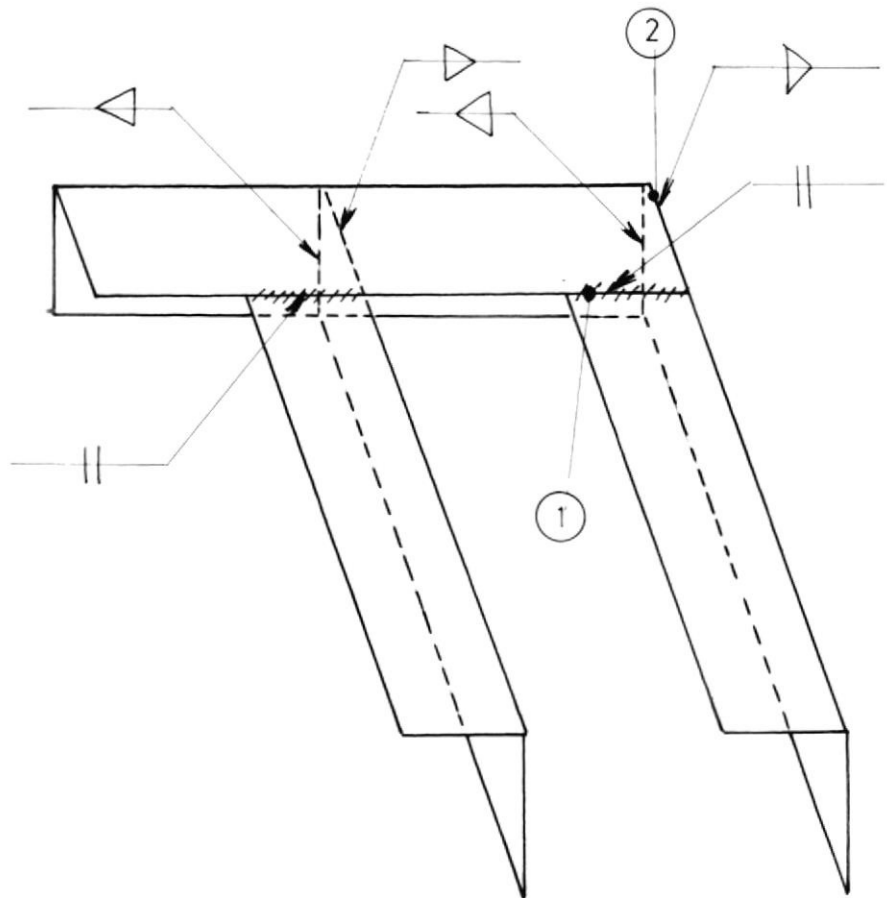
ESQUEMA DE LAS PARTES SOLDADAS DEL BASTIDOR.
